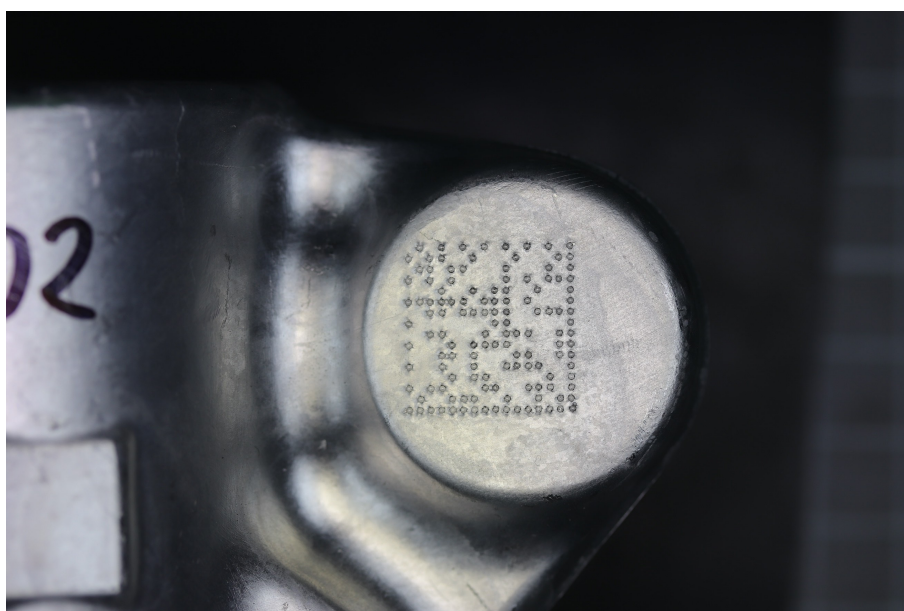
makro sken s měřením v 2. směru (tmavý)
